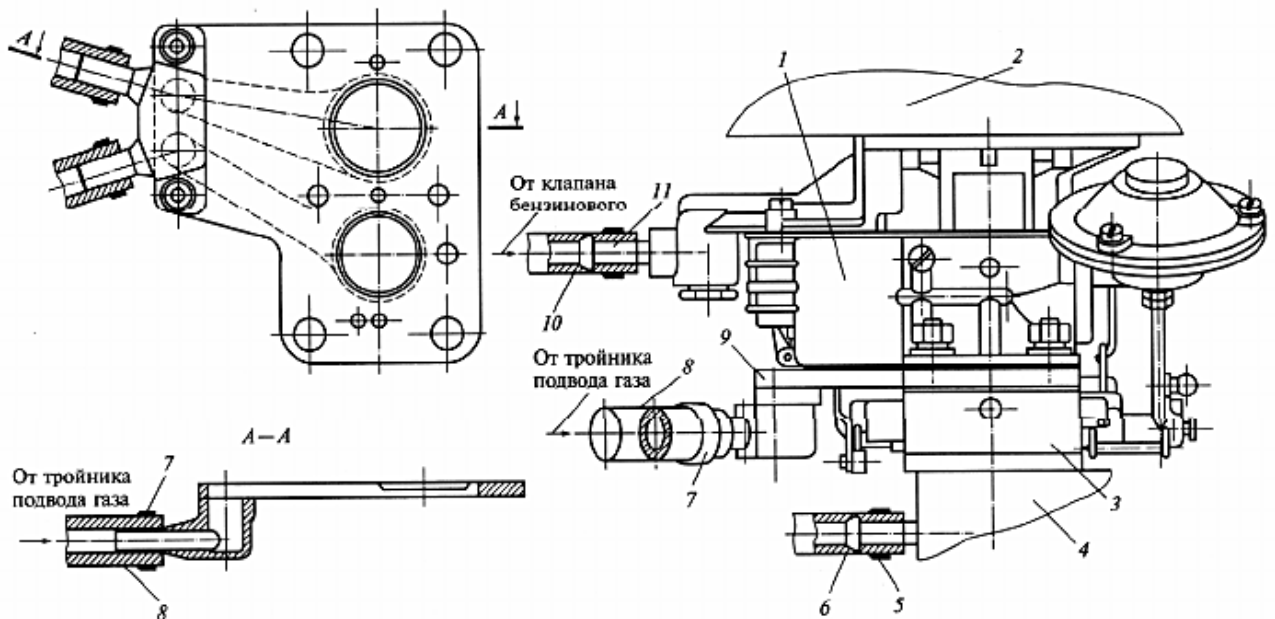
Газовый смеситель-проставка ЗАО «Автосистема» на карбюраторе «Озон»: 1 – средняя часть корпуса карбюратора; 2 – воздушный фильтр; 3 – нижняя часть карбюратора; 4 – впускной коллектор; 5, 7 и 11 – хомуты; 6 – патрубок подвода теплоносителя; 8 – патрубок подвода газа; 9 – проставка-смеситель; 10 – штуцер подвода бензина.
